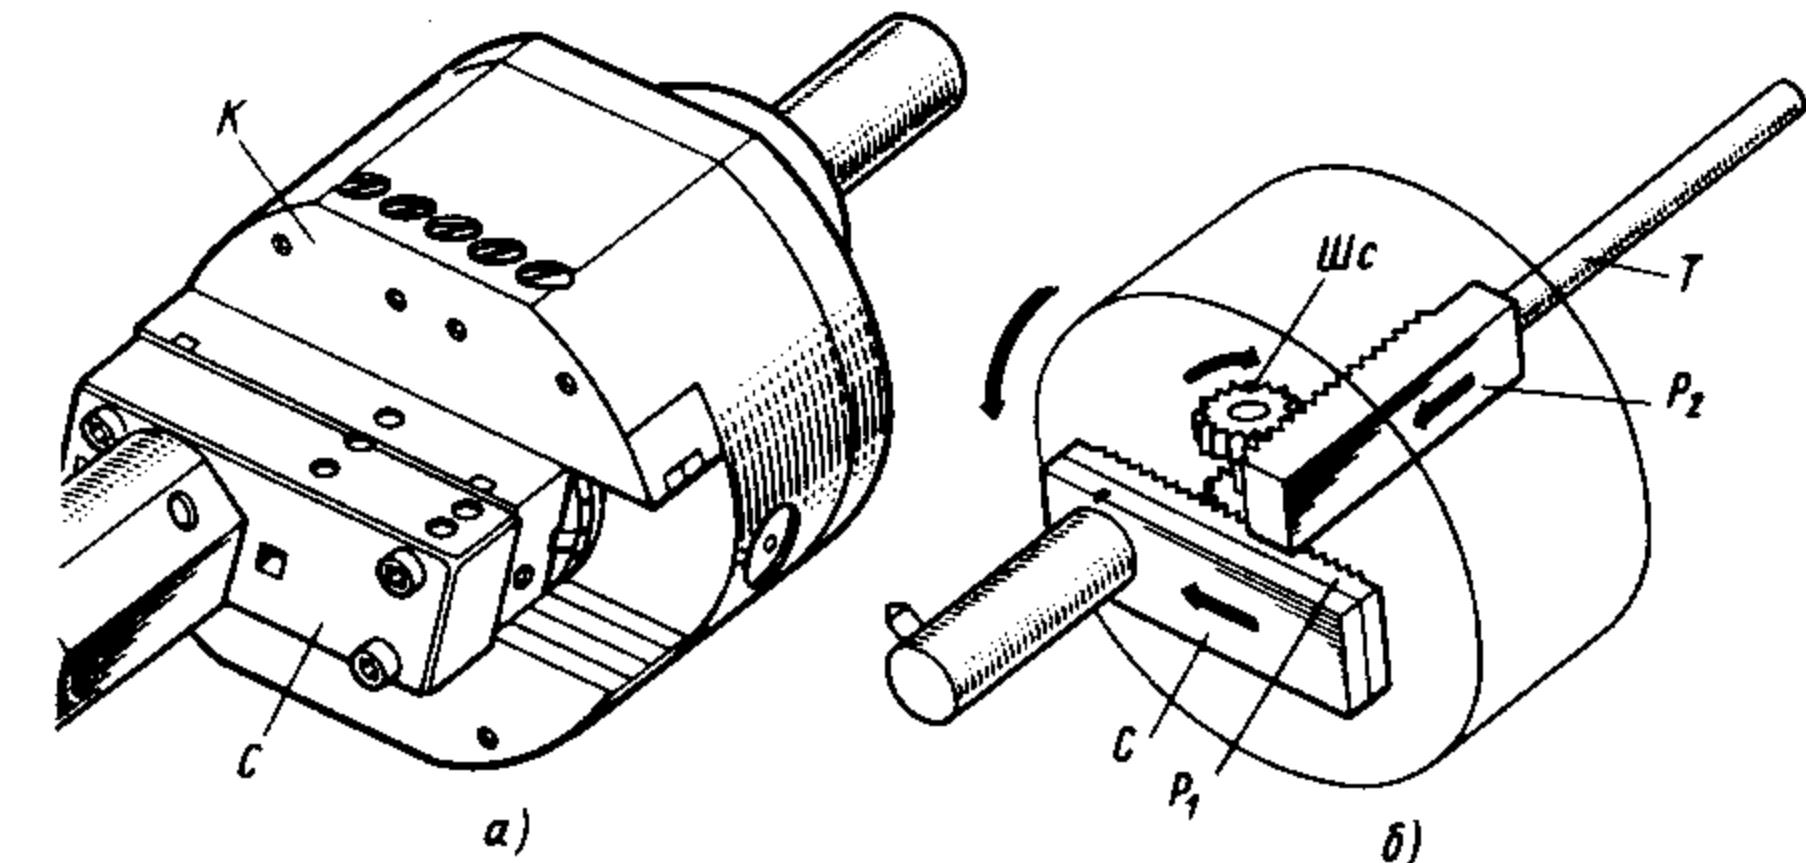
Плансуппортная головка: а – общий вид; б – устройство
